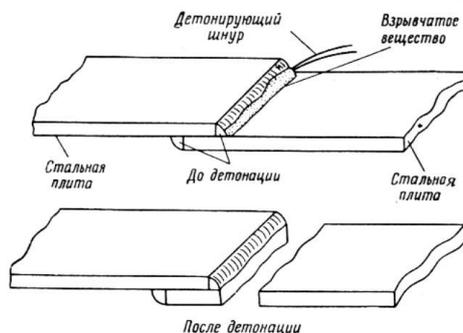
Резка сварной плиты контактным зарядом
